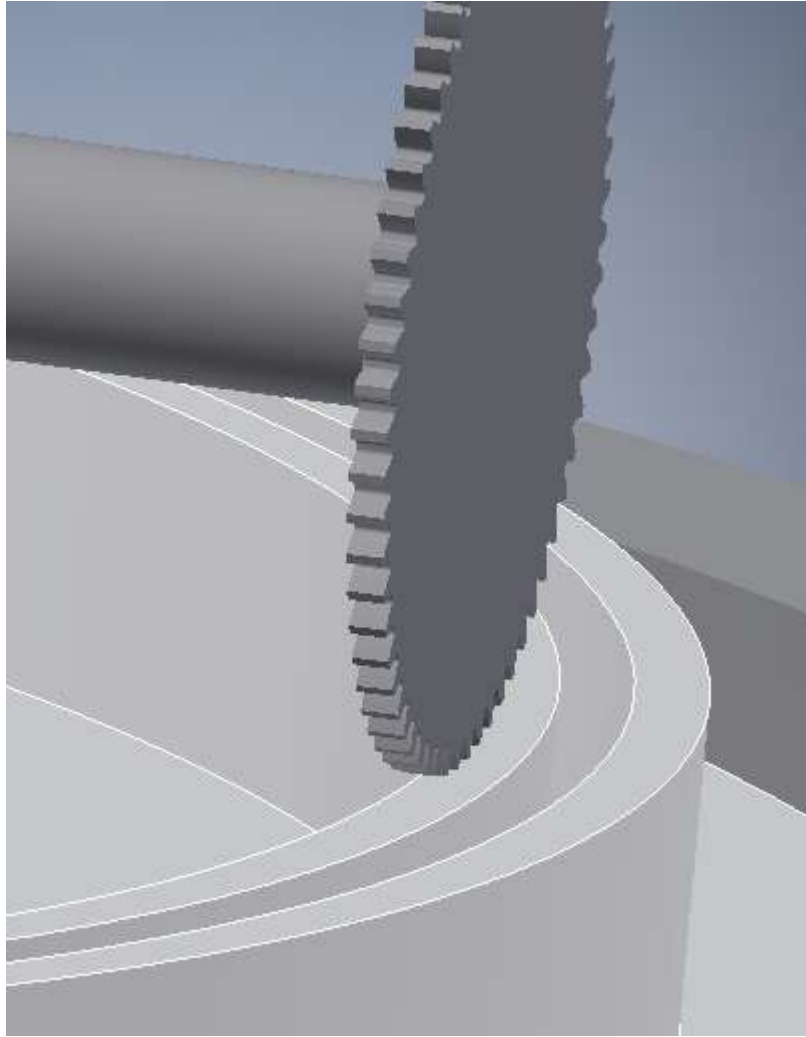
Detalle del contacto entre engranaje A y engranaje plano interior.
